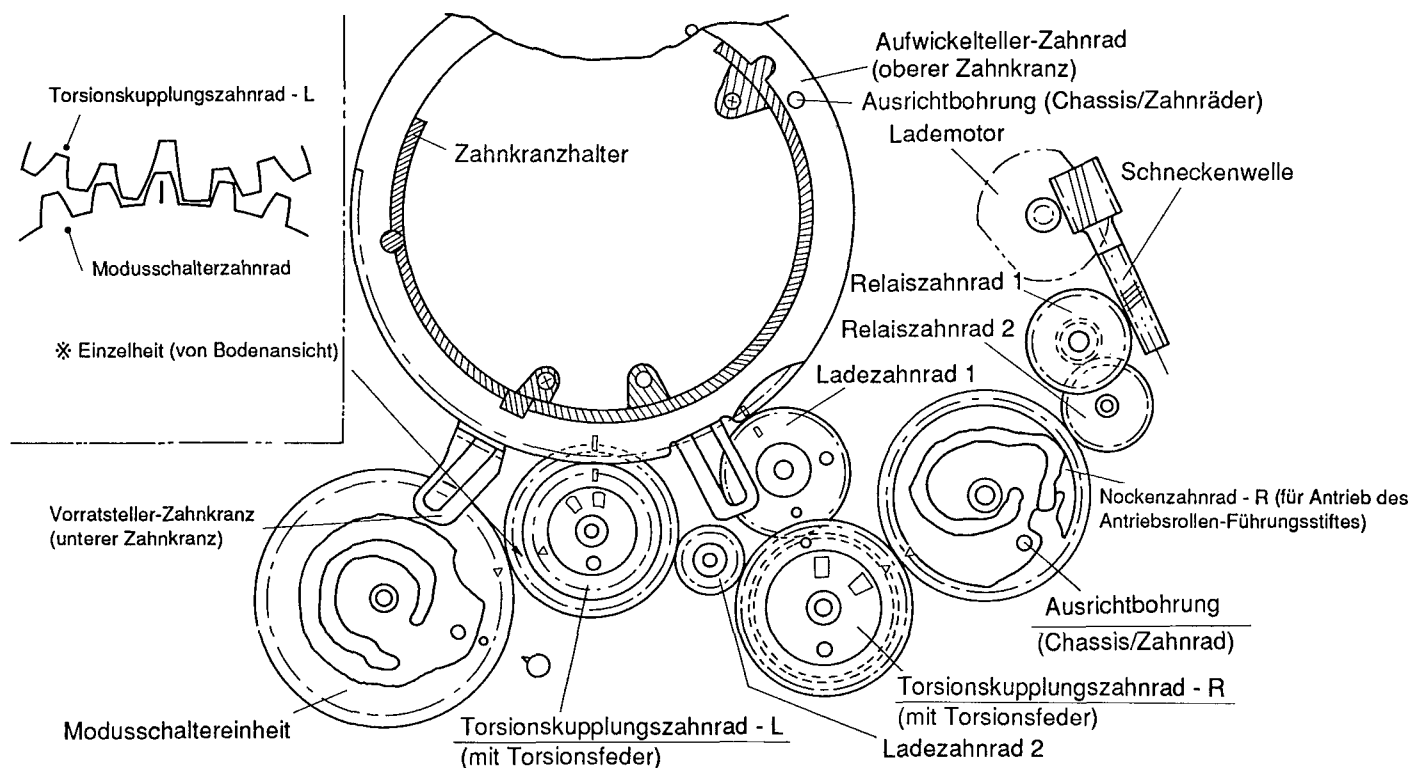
Lademechanismus des TH-Chassis (Draufsicht)
